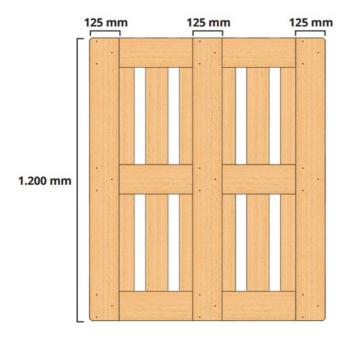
Esquema de vista inferior de um pallet com tábuas inferiores com 1200 mm de comprimento e 125 mm de largura.
